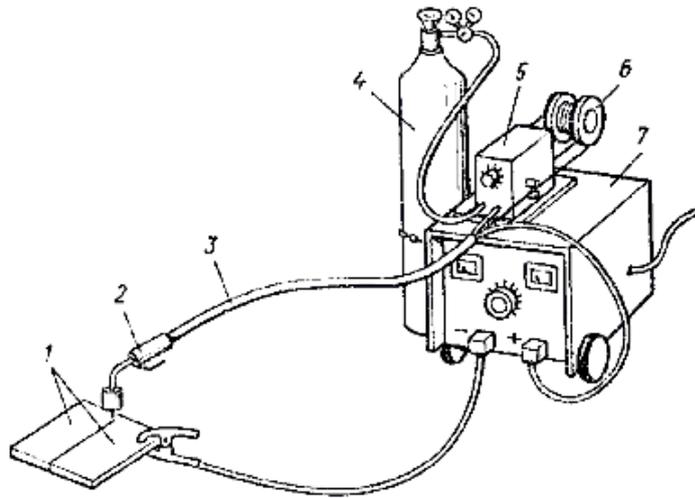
Сварочный пост полуавтоматической дуговой сварки в среде аргона
